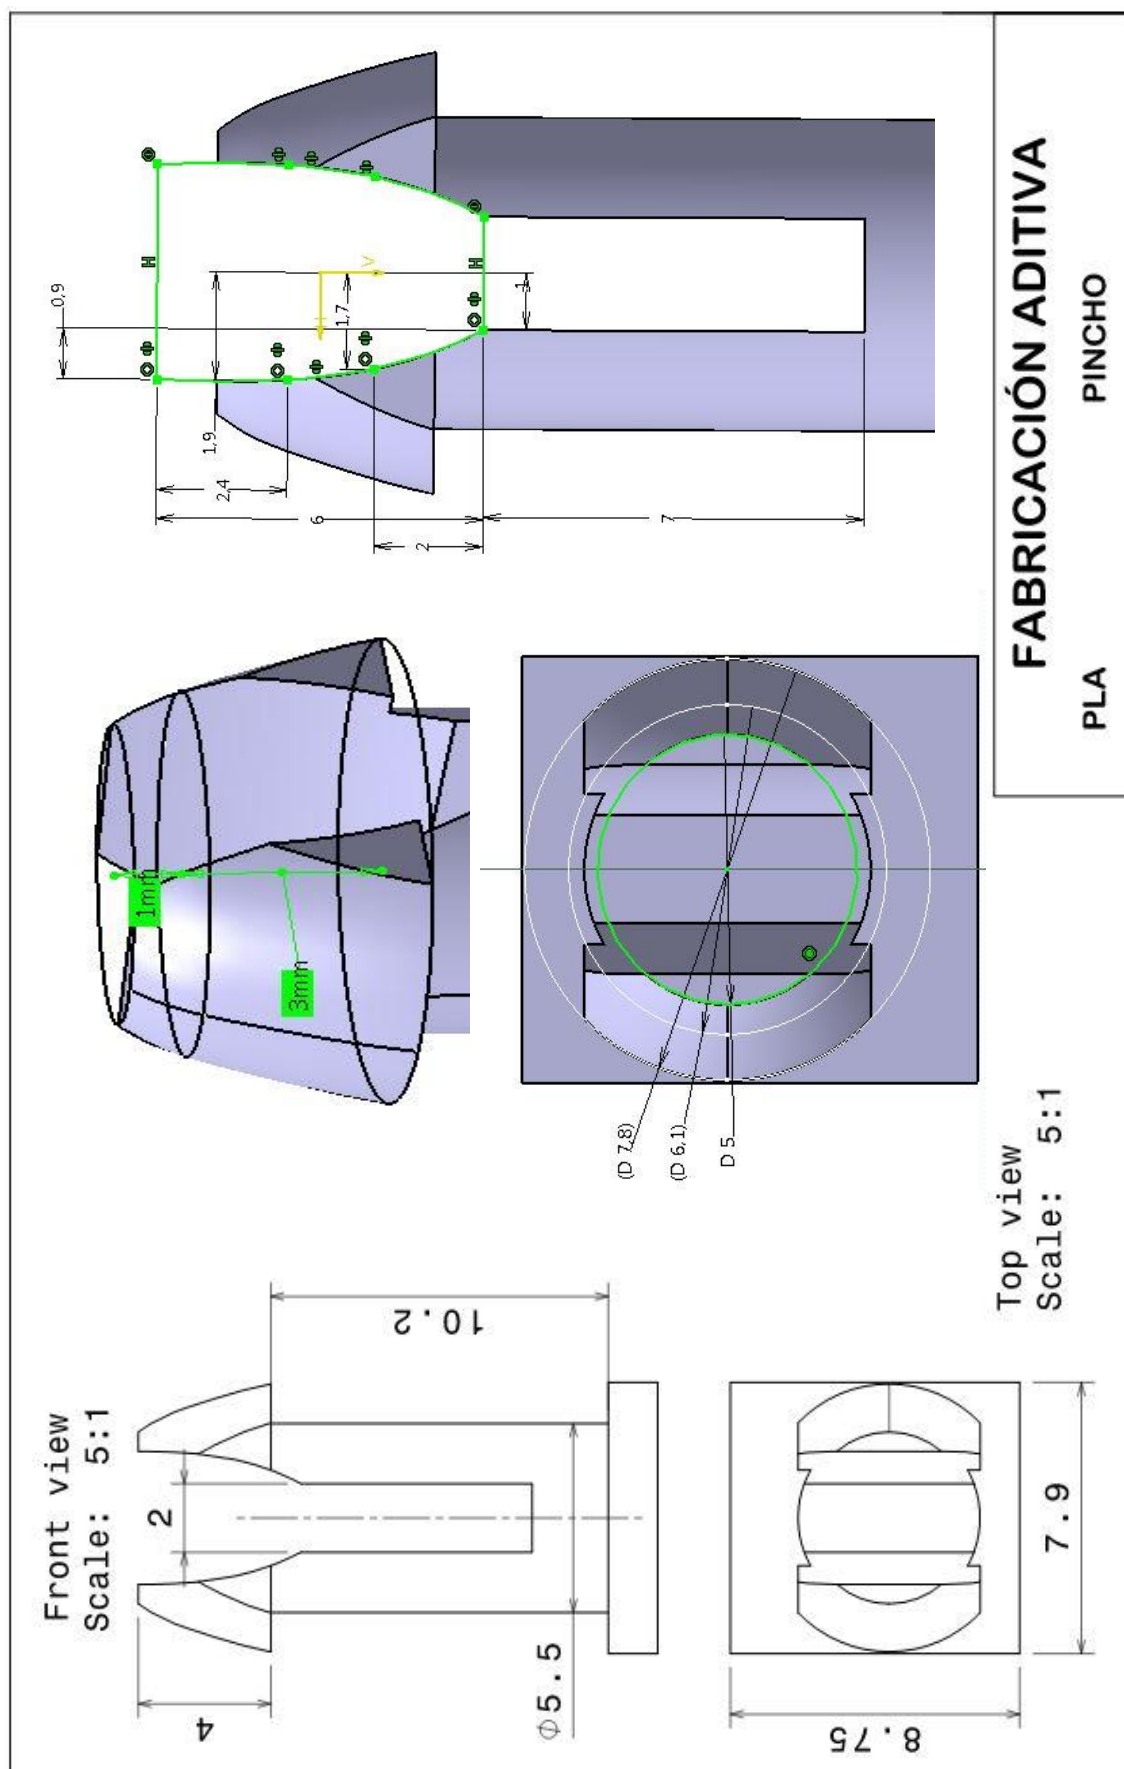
Planos pincho de ensamblaje de la carcasa.
